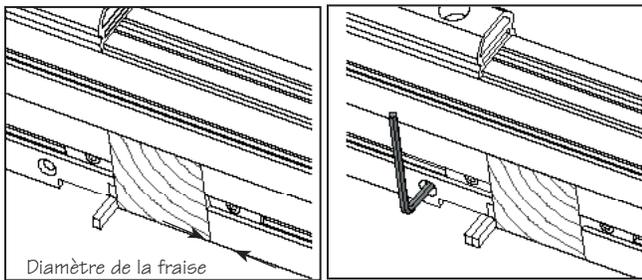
Montage de la cale fixe pour les queues droites de 1/8 po (3 mm) de largeur.
